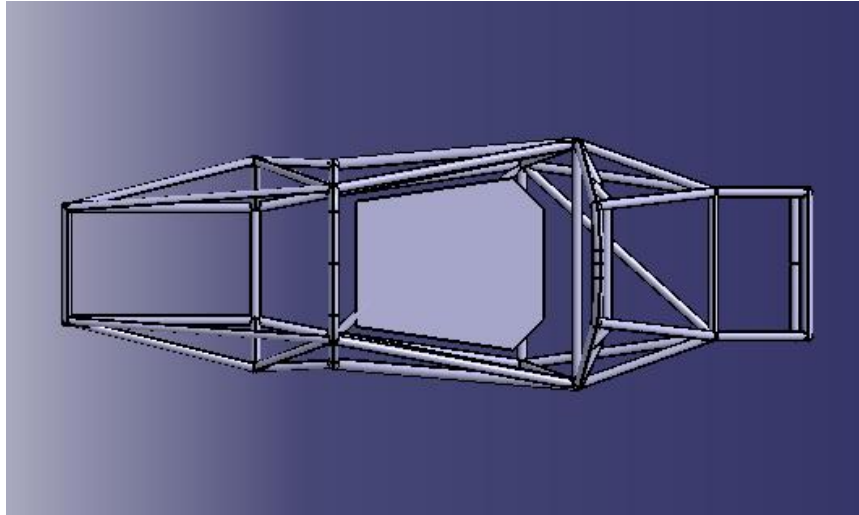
Vista en planta del xassís amb el pilot situat en la posició central. Font pròpia.
